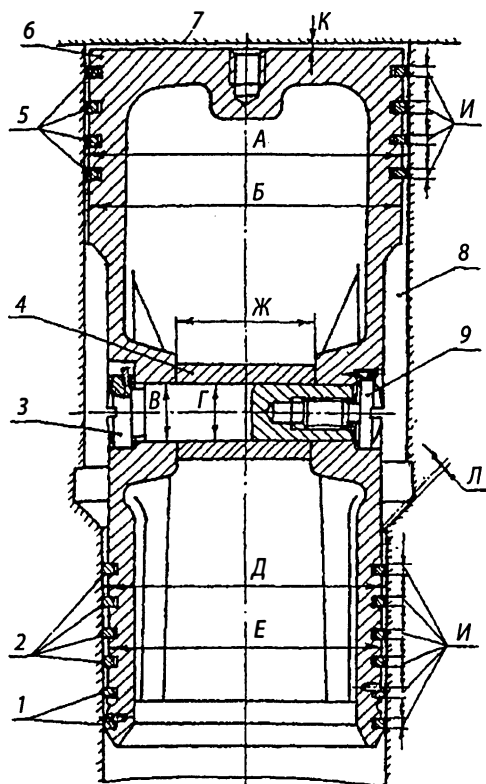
Поршень: 1 — кольца маслосъемные, 2 — кольца поршневые, 3 — поршневой палец, 4 — втулка, 5 — кольца поршневые, 6 — поршень, 7 — крышка цилиндра, 8 — цилиндр, 9 — винт
